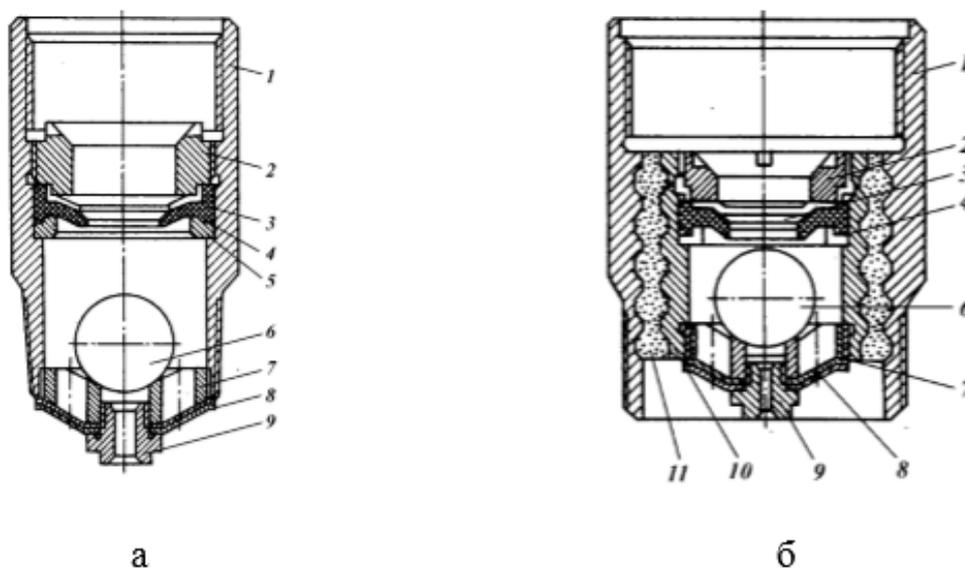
Клапаны обратные: а – ЦКОД-1, б – ЦКОД-2: 1 – корпус; 2 – нижняя гайка; 3 – пакет резиновых шайб; 4 – резиновая диафрагма; 5 – опорное кольцо; 6 – шар; 7 – ограничительное кольцо; 8 – резиноканевая мембрана; 9 – дроссель; 10 – чугунная втулка; 11 – бетонная или пластмассовая подвеска
